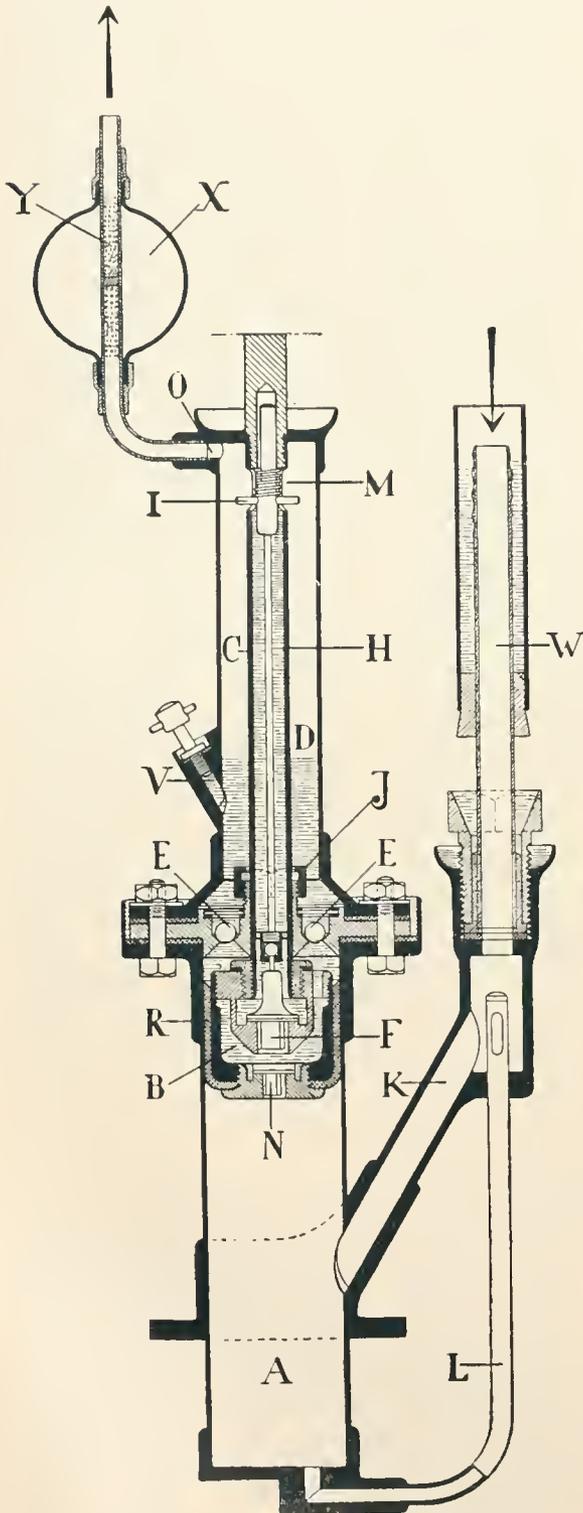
Durchschnitt einer Luftpumpe mit Öldichtung.
